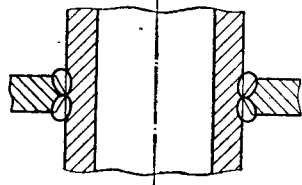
Схема сварного соединения для металлографического исследования качества сварки.
